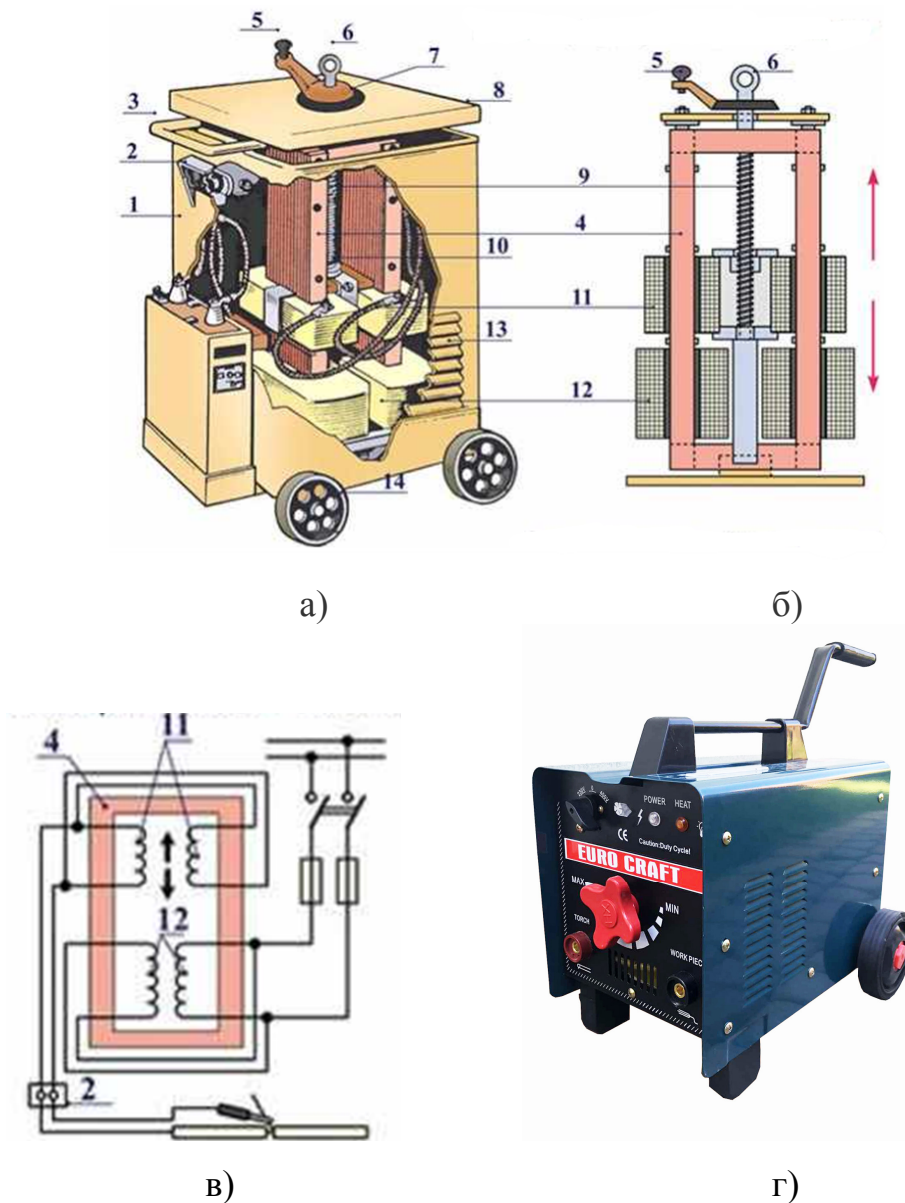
Зварювальний трансформатор: а, г - загальний вигляд; б - схема регулювання зварювального струму, в - електрична схема; 1 - корпус; 2 - клемми; 3 - ручка; 4 - замкнений магнітопровід; 5 - рукоятка; 6 - рим - болт; 7 - шкала; 8 - кришка корпусу; 9 - вінт з лентою для різки; 10 - ходова гайка; 11 - вторина обмотка; 12 - первина обмотка; 13 - жалюзі; 14 - колеса.
